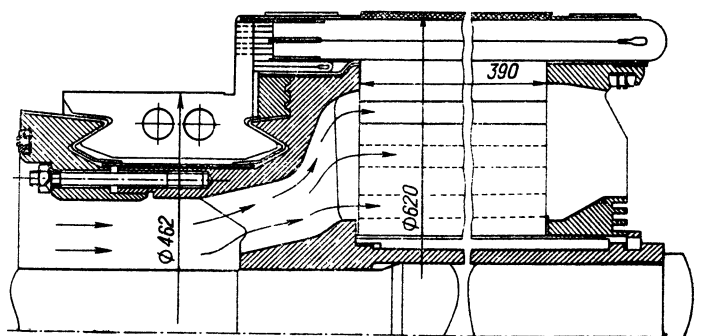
Якорь тягового двигателя ТАО-649В1
